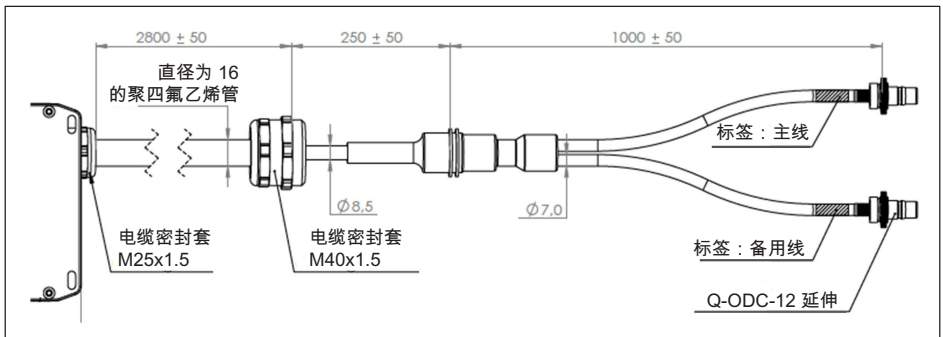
互连盒 - 电缆一侧 - 技术图纸 (尺寸单位为 mm)
